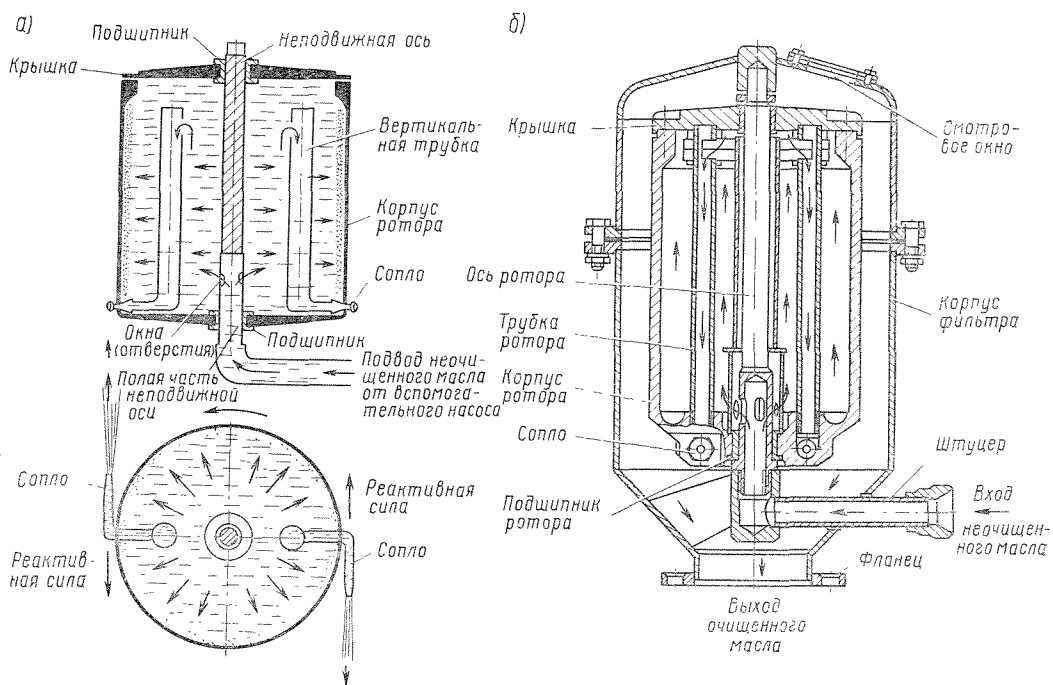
Центробежный фильтр очистки масла: а — схема работы; б — схема устройства
